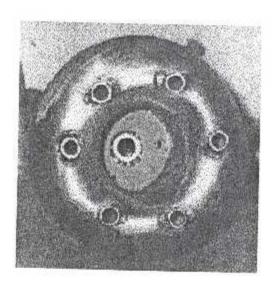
Tuyauteric carburant et son emplacement sur la chambre.
